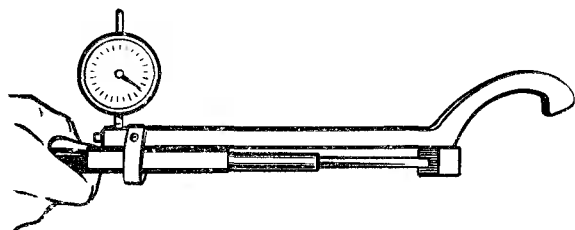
Проверка затяжки подшипников динамометрической рукояткой
